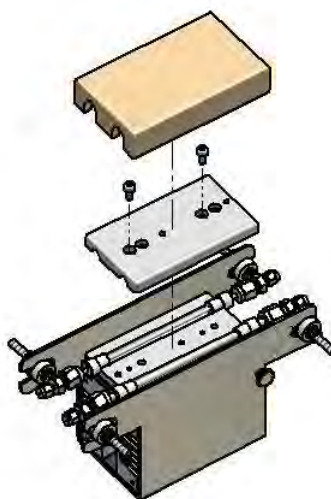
Explosionszeichnung des Peltier-Kühlers
